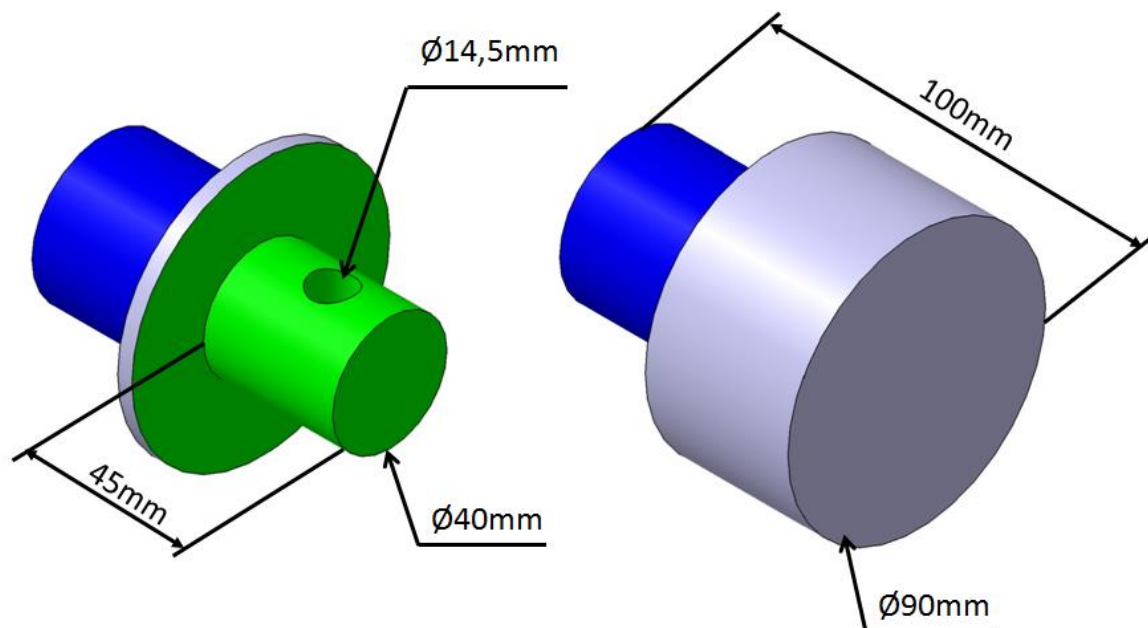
Testwerkstück für Drehmaschinen nach Brillinger M.
